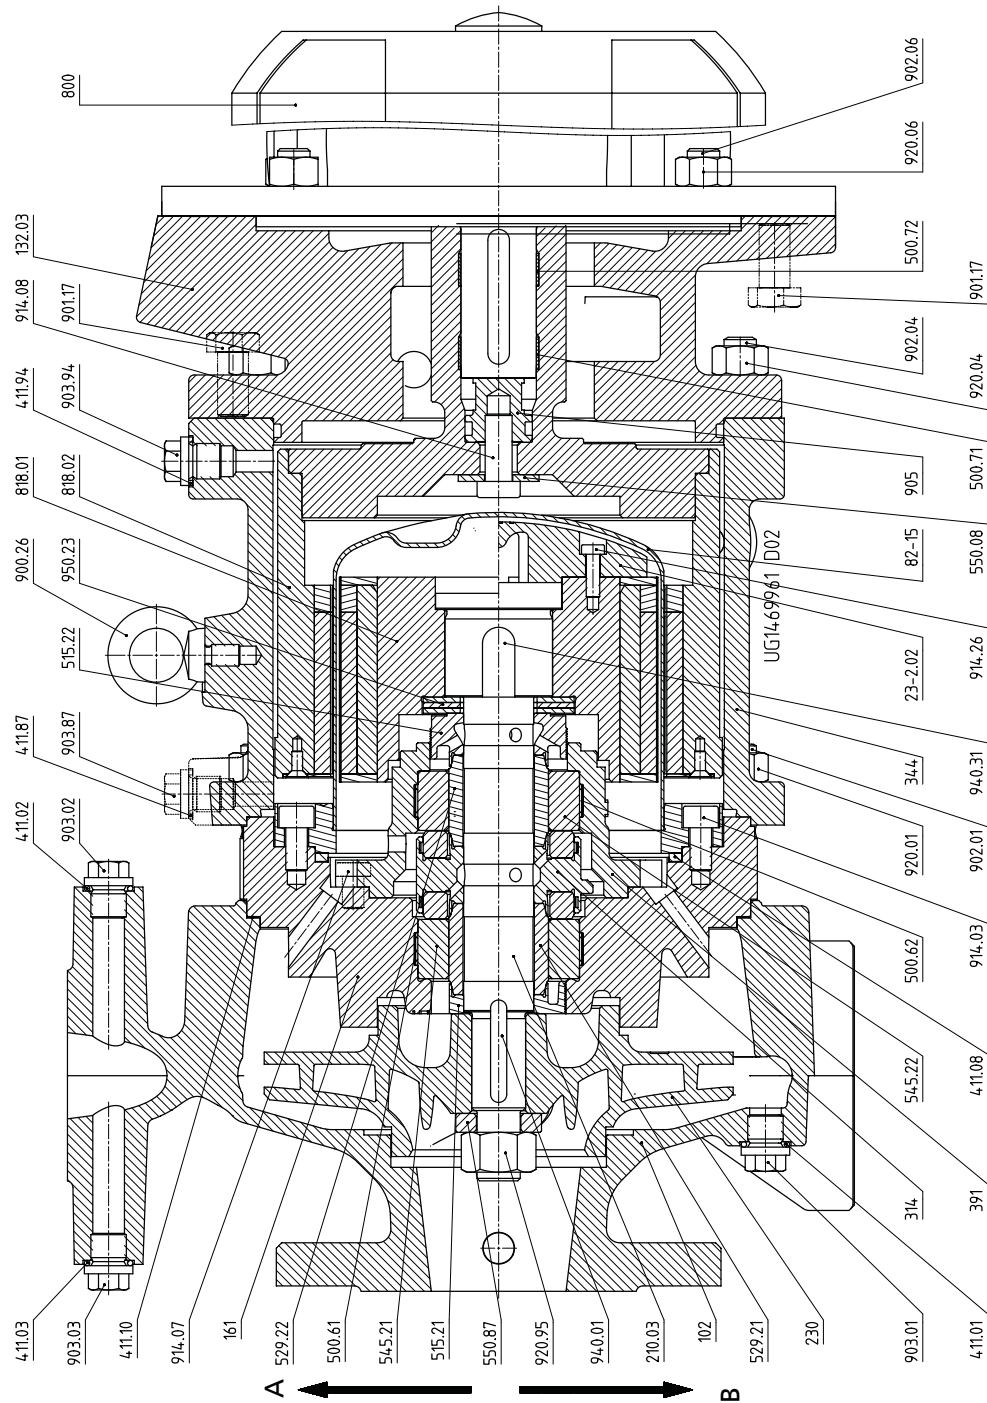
Gesamtzeichnung Ausführung mit geklemmtem Deckel ohne Zwischenstück
